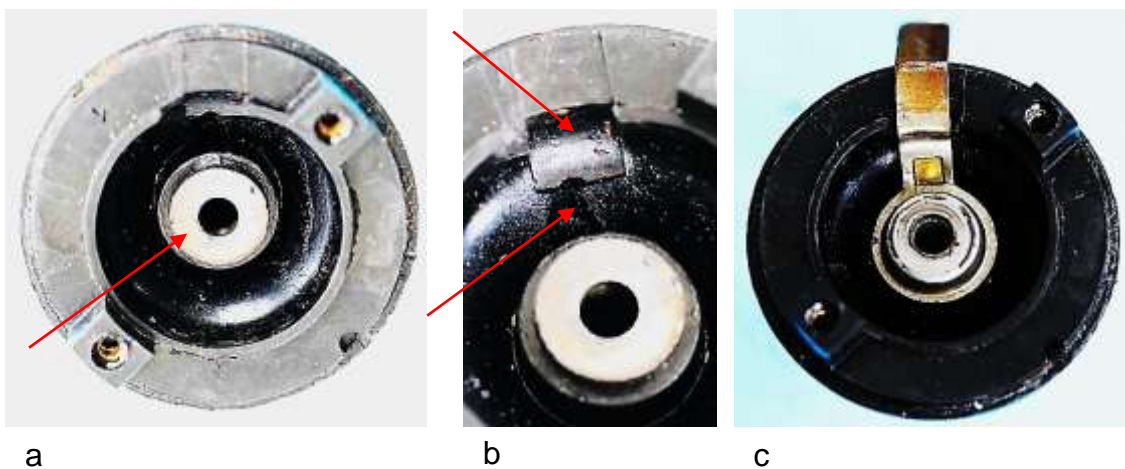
Anbringung des Massekontakts im Lagerhalsfuß: a) Lagerhalsfuß mit Lager, b) Nut für die Blechzunge und Bohrung für die Blattfeder, c) Eingefügter Massekontakt
